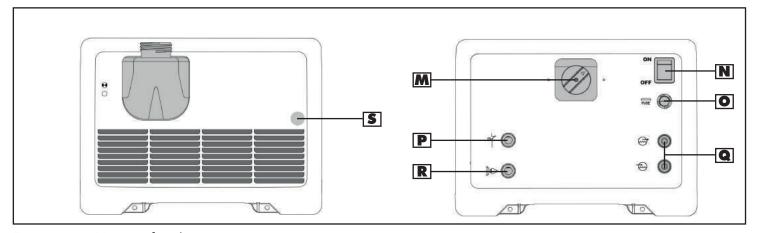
Unitè refroidissement par eau - vue avant et arrière
